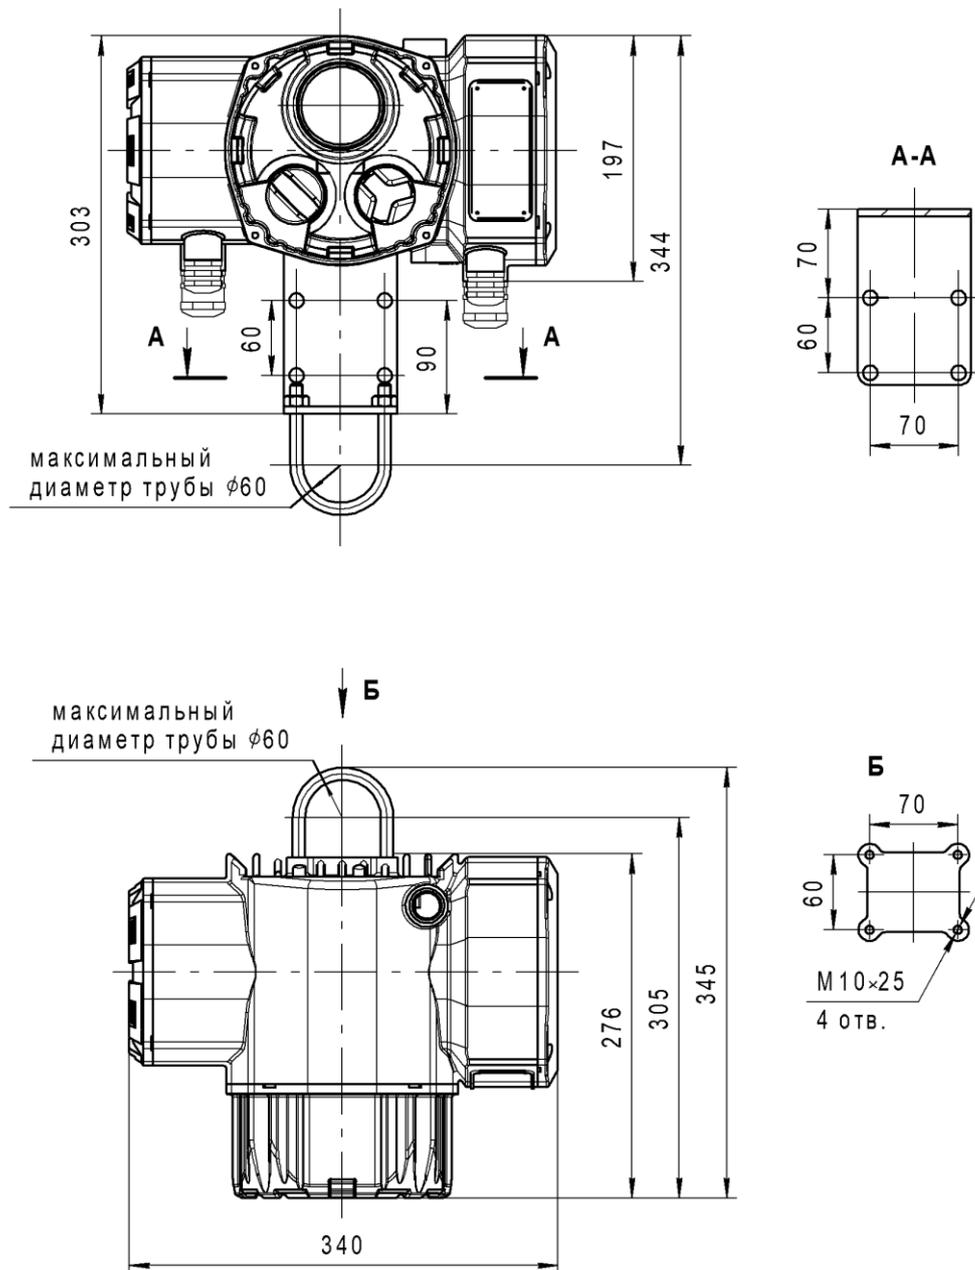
Габаритные и присоединительные размеры выносного блока управления
